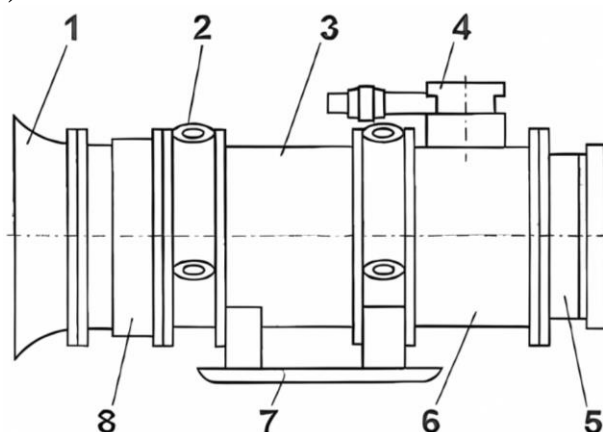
Вентилятор ВМ-6 (ВМ-6/1): 1 – подвод с решеткой; 2 – проушина; 3 – корпус; 4 – ввод силового кабеля; 5 – выходной патрубок; 6 – электродвигатель исполнения РВ; 7 – салазки; 8 – противосрывное устройство
